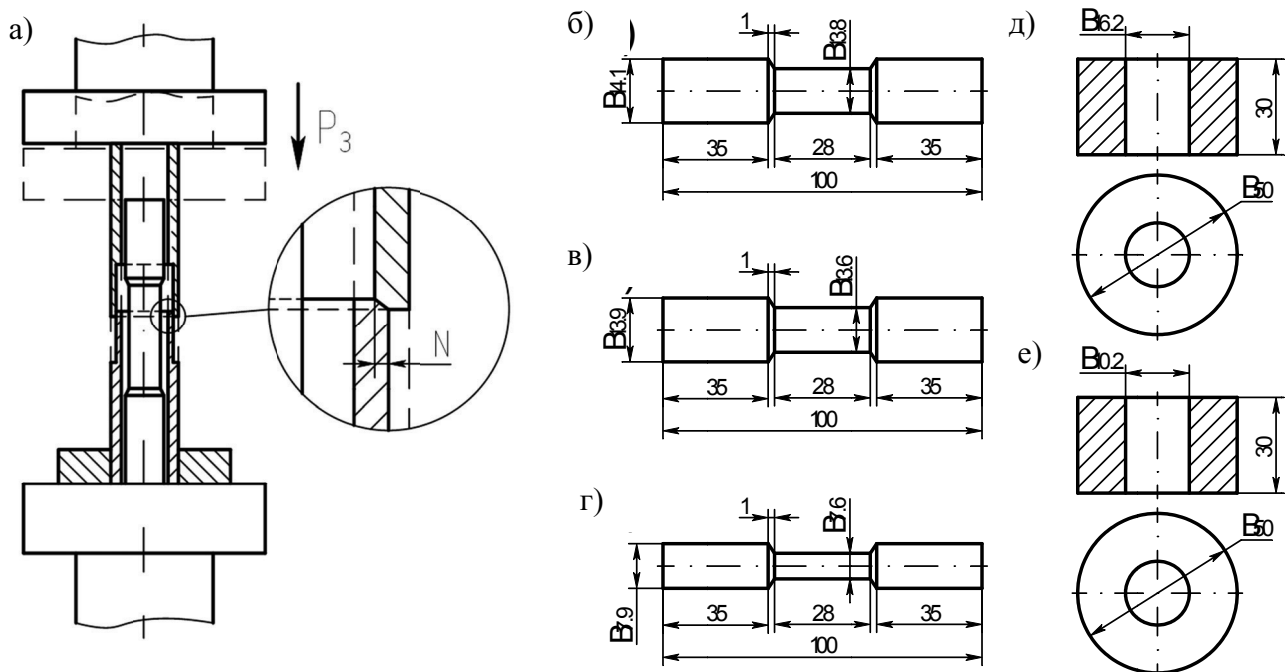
Схема получения прессового соединения: а – схема запрессовки образцов; б – центрирующий штифт для титановых образцов; в – центрирующий штифт для алюминиевых образцов; г – центрирующий штифт для стальных образцов; д – опора для титановых и алюминиевых образцов; е – опора для стальных образцов;
